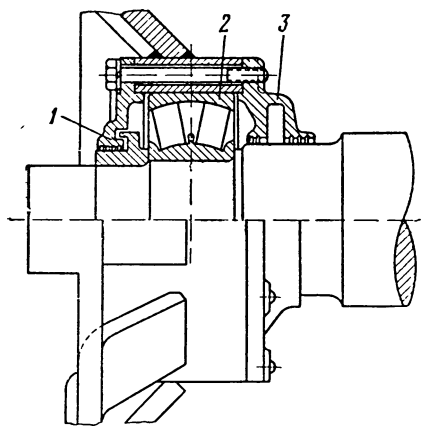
Подшипниковый узел генератора с внутренней крышкой новой конструкции:
